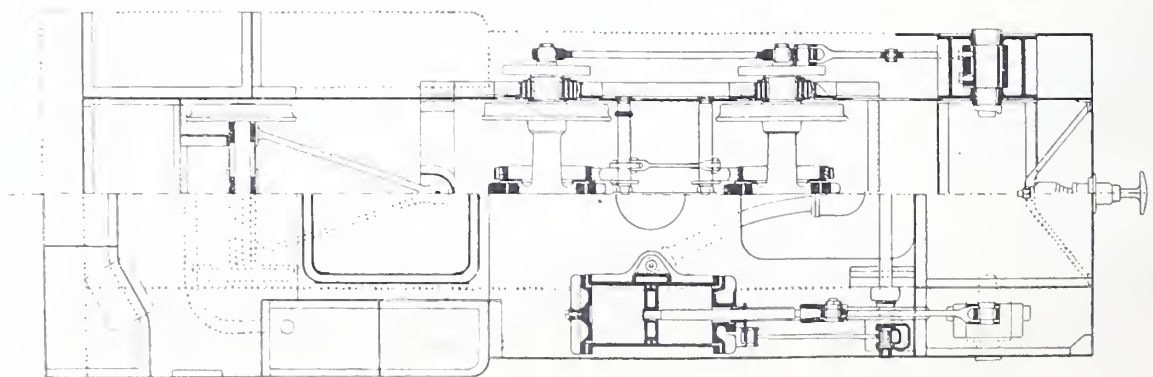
Grundriss und Horizontalschnitt.
